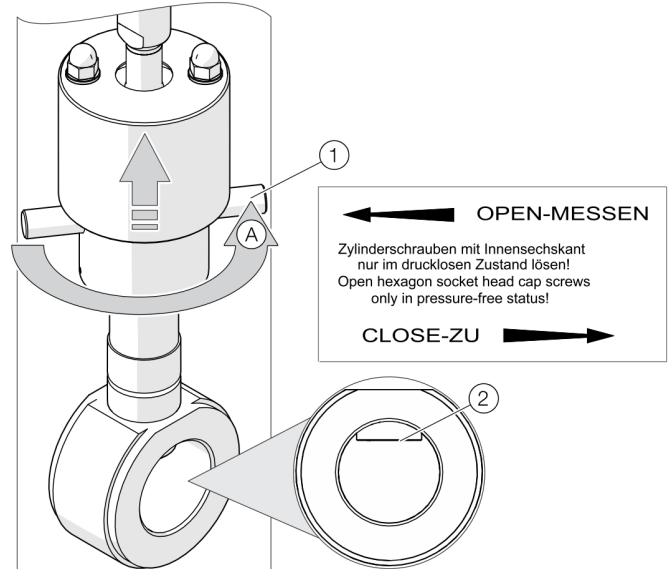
Colocar o dispositivo de mudança integrado na posição de desmontagem
